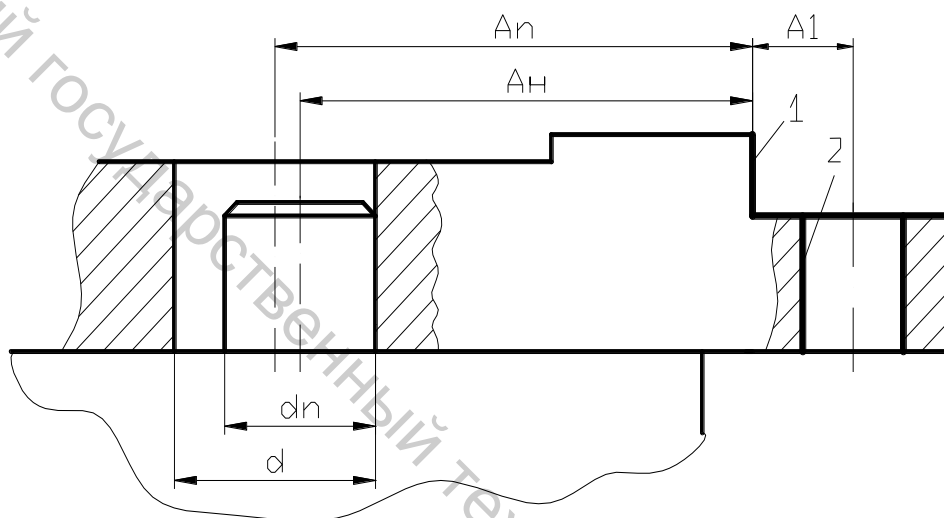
Установка заготовки по отверстию на цилиндрический палец
